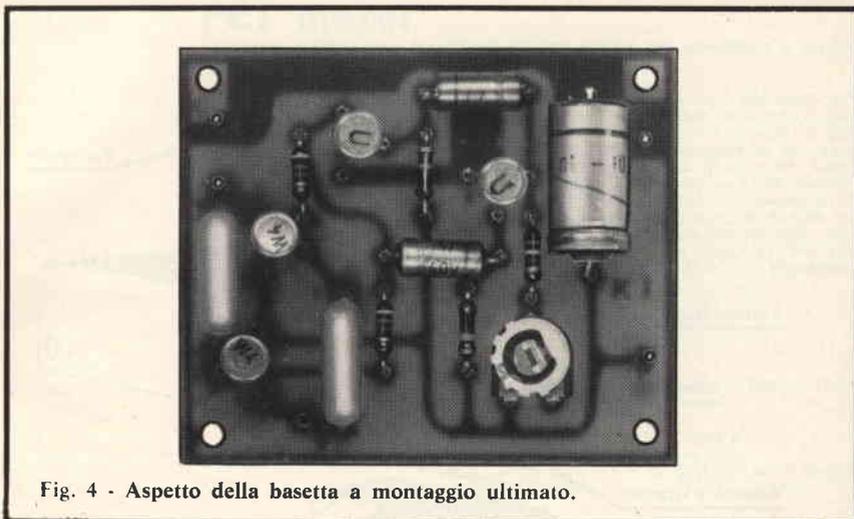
Aspetto della bassetta a montaggio ultimato.
